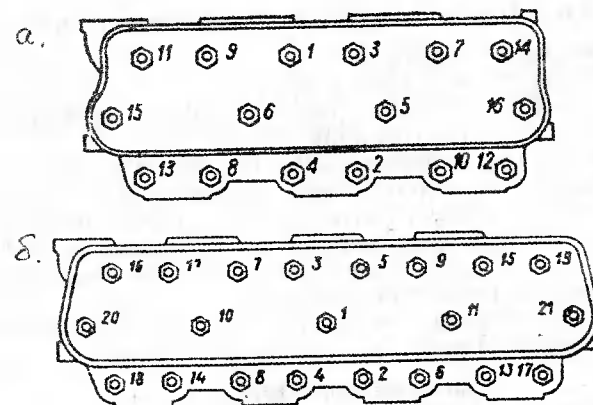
Последовательность затяжки гаек крепления головок цилиндров: а — двигателя ЯМЗ-236М; б — двигателя ЯМЗ-238М, ЯМЗ-7511.10
